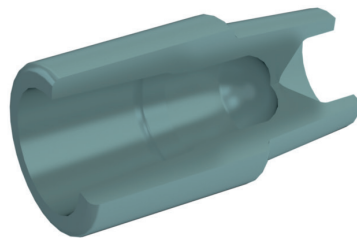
3D-модель, поковка «ниппель нефтегазовой арматуры»
